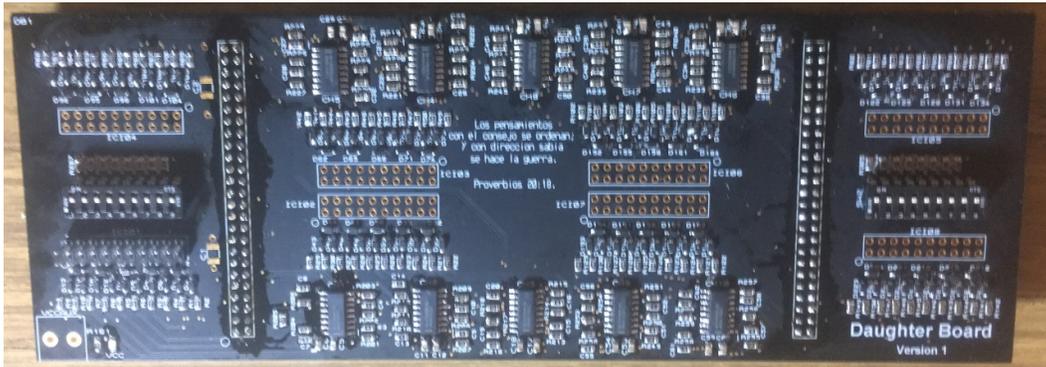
Proceso de soldado de la Daughter Board. Vista superior.
